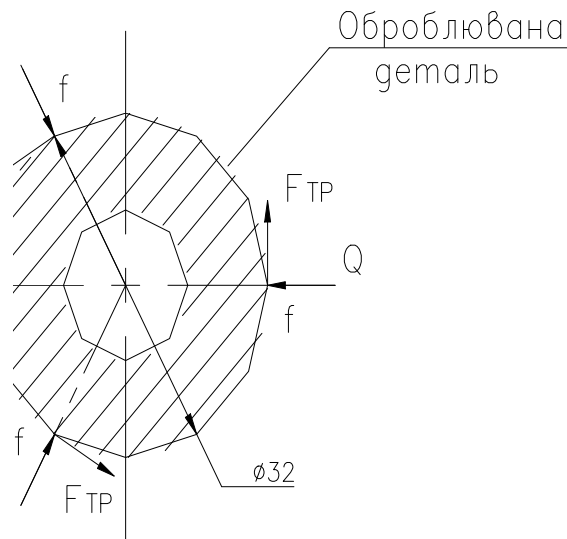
Розрахункова схема для визначення затискної сили пристрою Q.
